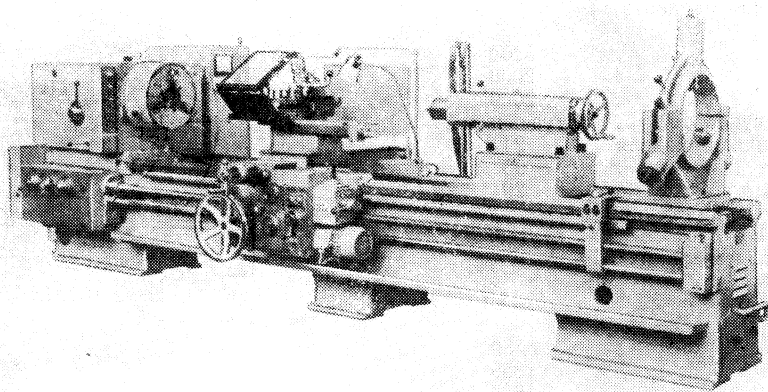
Общий вид токарно-винторезного станка мод. 16К40
